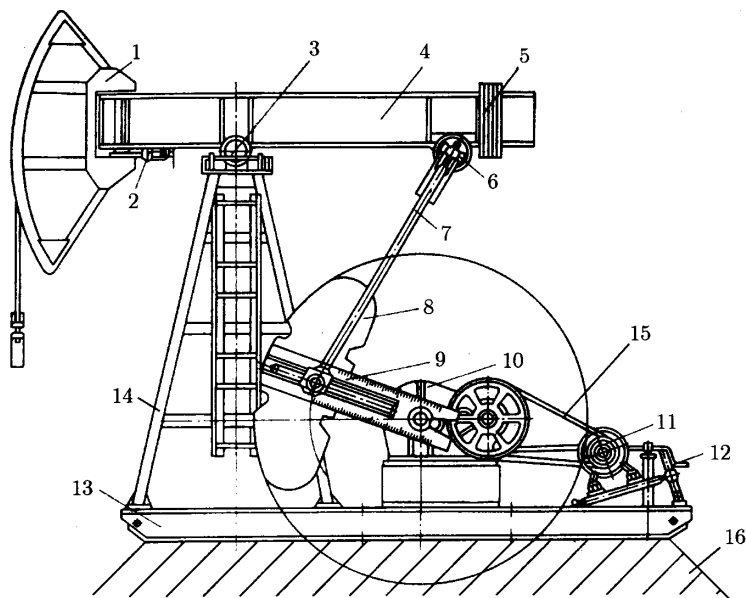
Станок качалка: 1 – головка балансира; 2 – стопорное устройство головки; 3 – опорный подшипник балансира; 4 – балансир; 5 – противовесы; 6 – сферический подшипник подвески траверсы; 7 – шатун; 8 – противовес кривошипа; 9 – кривошип; 10 – редуктор; 11 – электродвигатель; 12 – ручка тормоза; 13 – рама; 14 – стойка; 15 – клиновые ремни; 16 – фундамент
